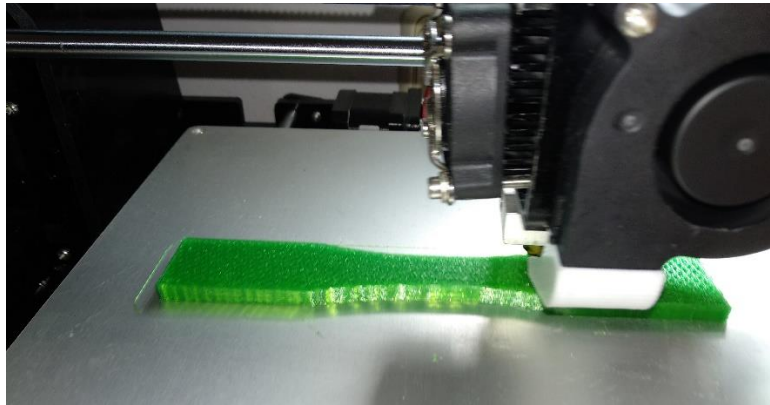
Probeta durante el proceso de impresión. Fuente: Autor.
